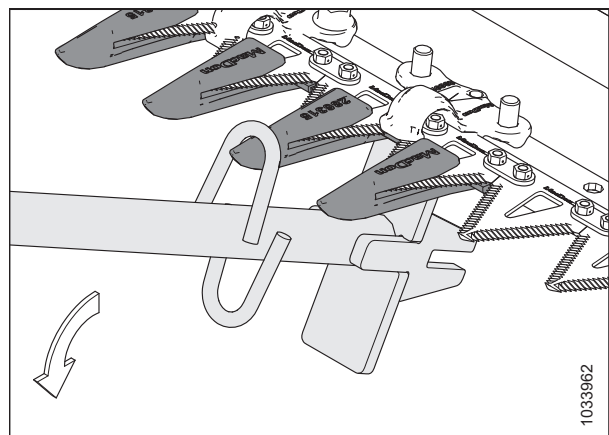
Регулювання верхнього положення — загострений протиріжучий палець
